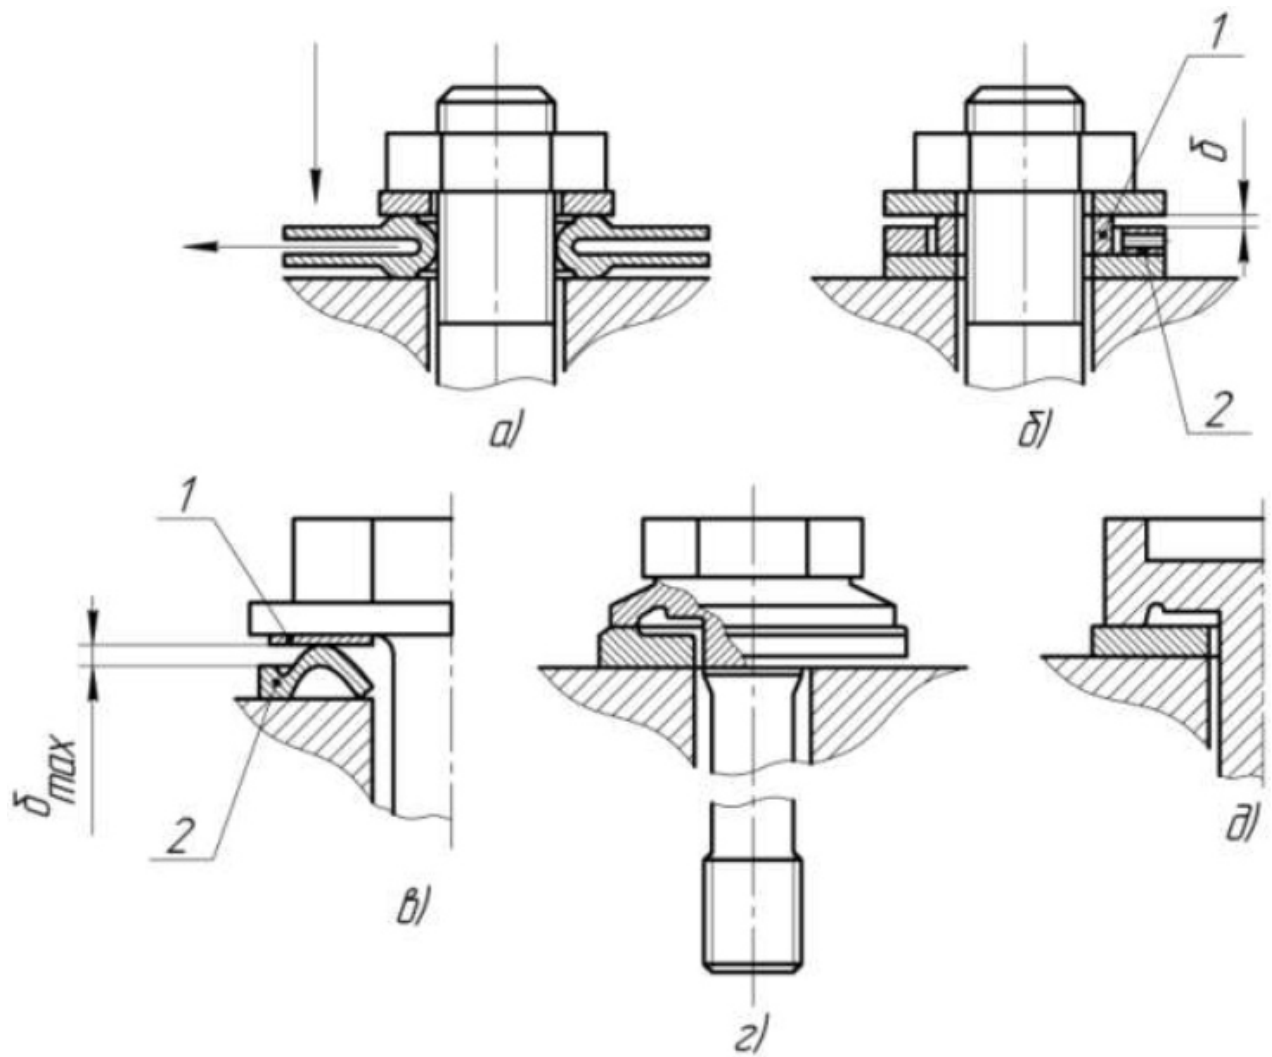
Шайби для вимірювального контролю величини сили затягування роз'ємних з'єднань
